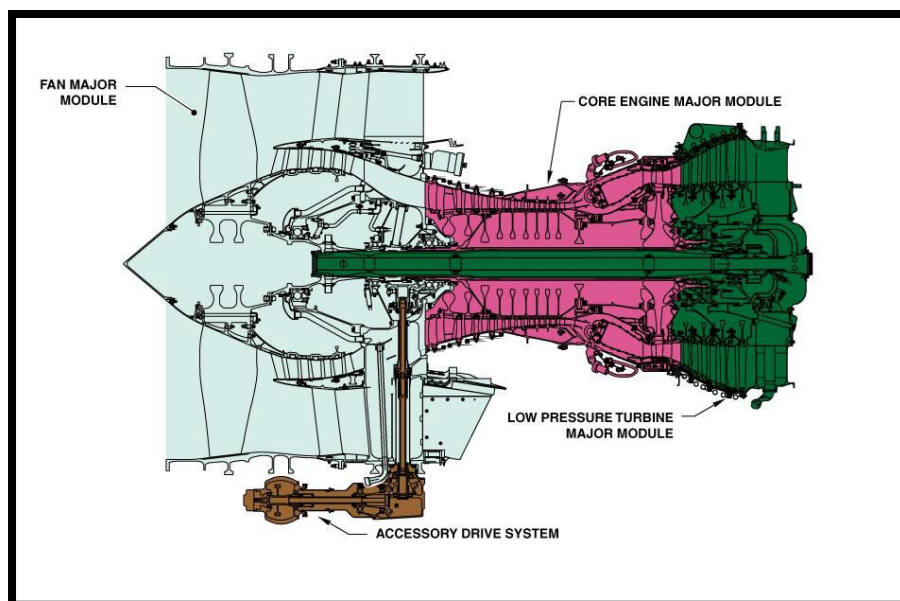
Esquema completo do motor, Fonte: COURSE OUTLINE CFM56-7B Basic Engine.:
